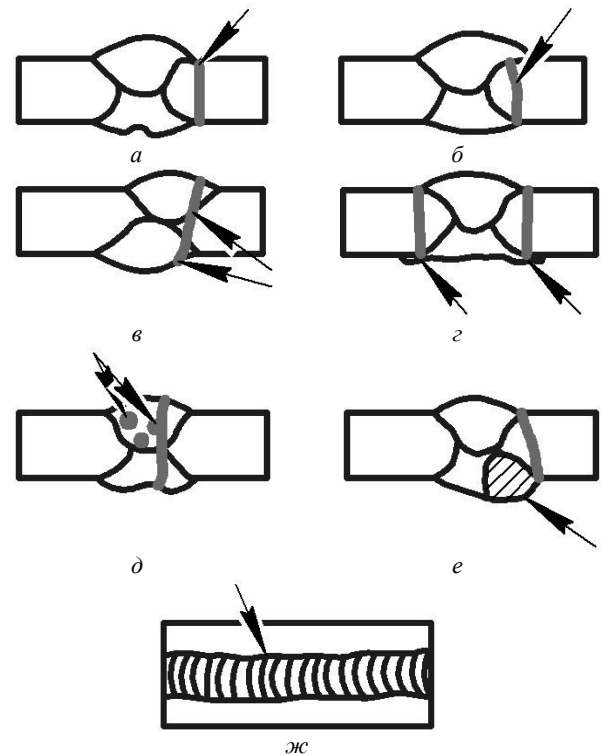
Схемы формирований дефектов сварных соединений трубопроводов, приводящие к разрушениям:
